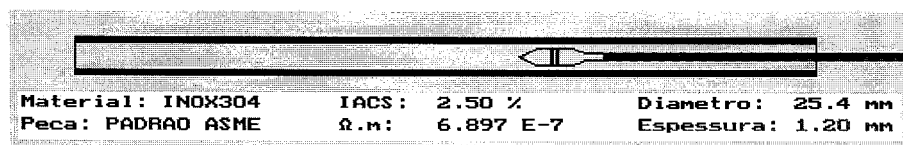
Um tubo a ser examinado, com a sonda de teste posicionada em seu interior.
